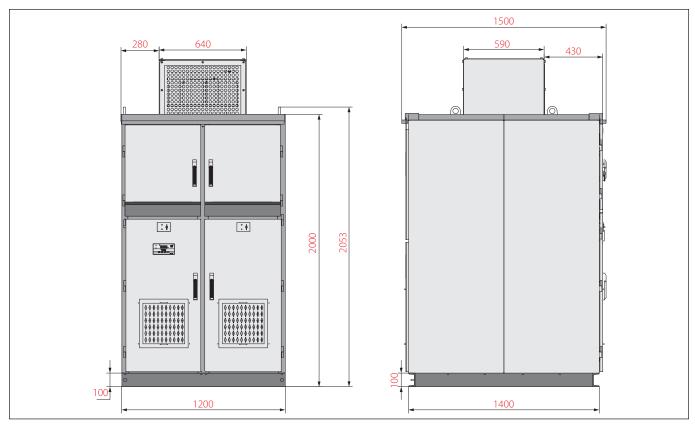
Корпус шкафа токоограничивающего реактора типоразмера ЕС01
